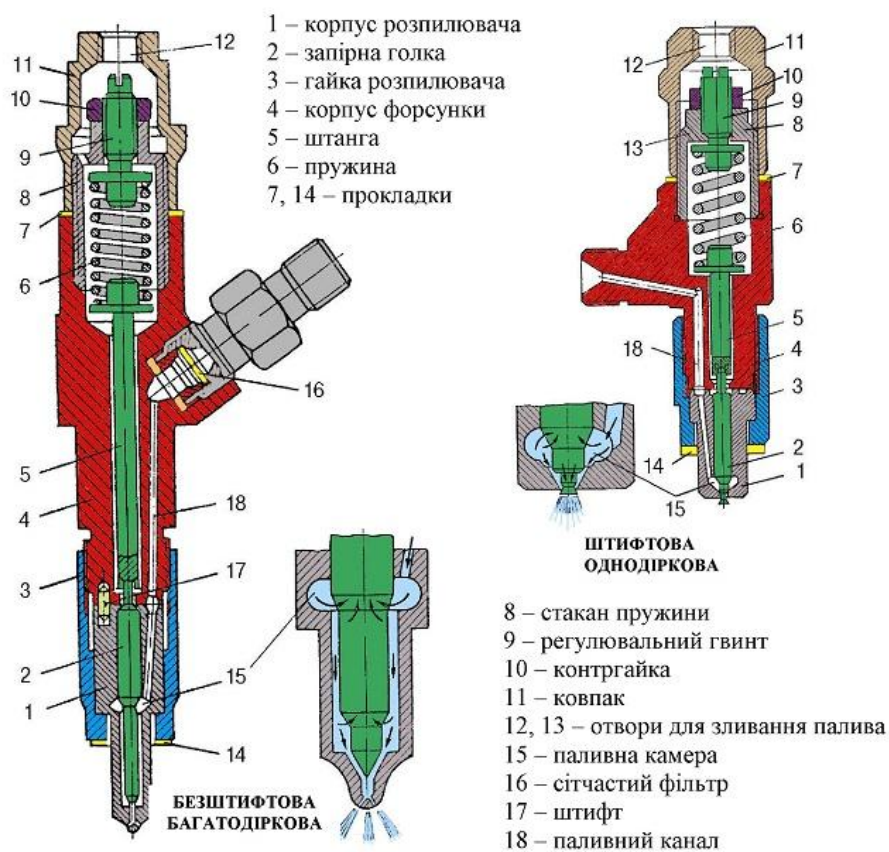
Форсунки і схема роботи їх розпилювачів
